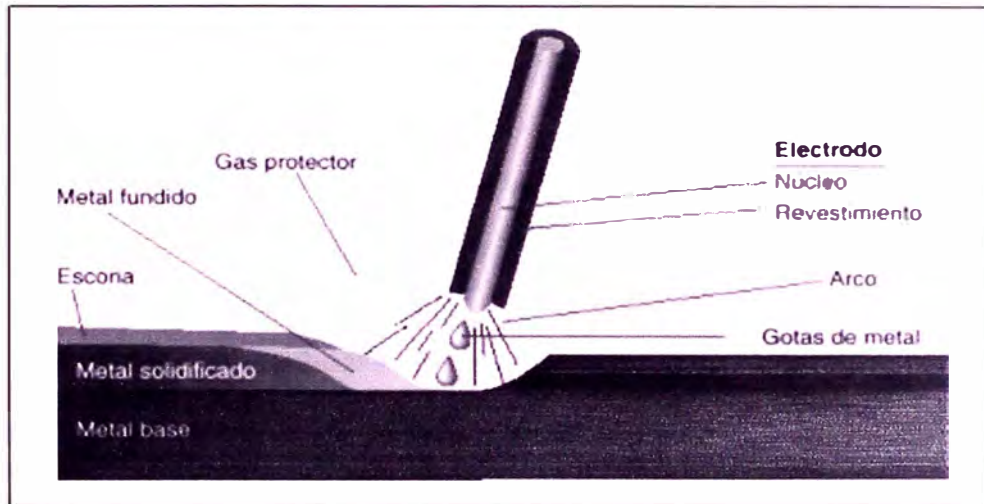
Proceso Soldadura manual con electrodo revestido.
